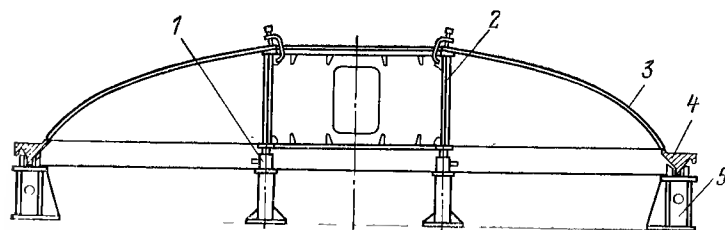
Стыковка днища страховочного кожуха с опорным кольцом.
